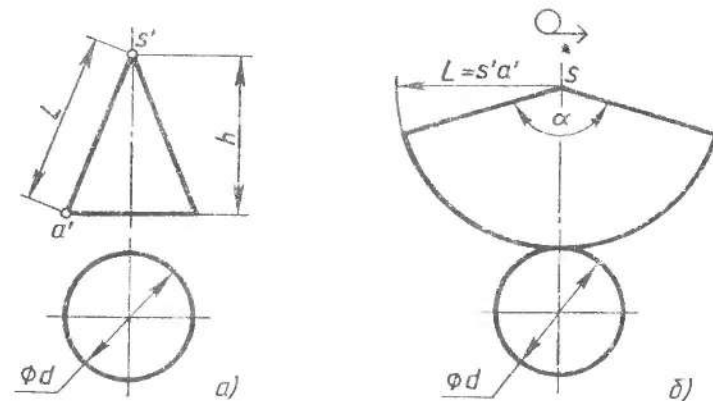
Построение чертежа развертки поверхностей конуса: а — два вида; б — развертка поверхностей
